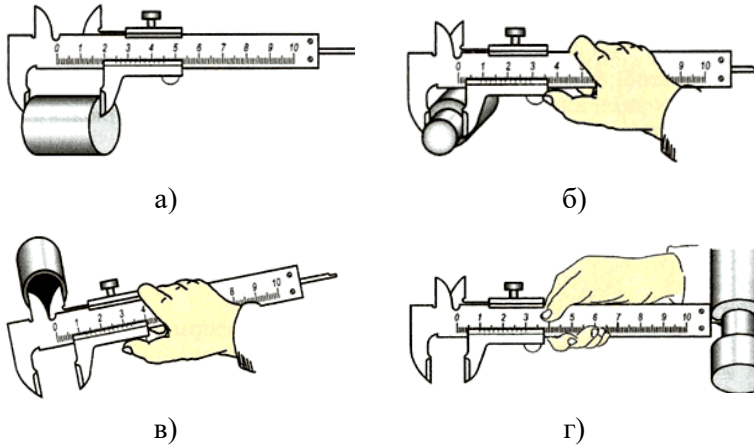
Вимірювання і контроль розмірів деталей штангенциркулем:
